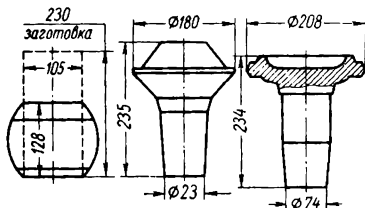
Штамповка поковки цапфы в три перехода, считая осадку
